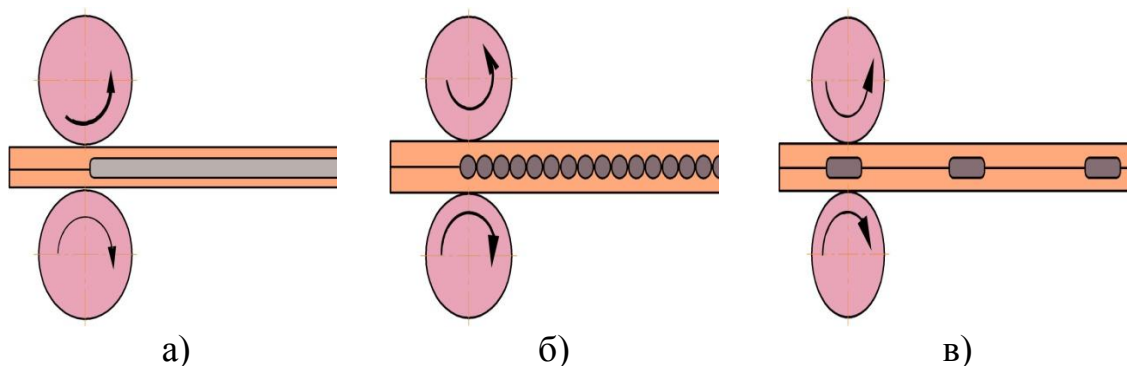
способы шовной сварки: а – непрерывная; б – прерывистую с непрерывным вращением роликов; в – прерывистую с периодическим вращением роликов
